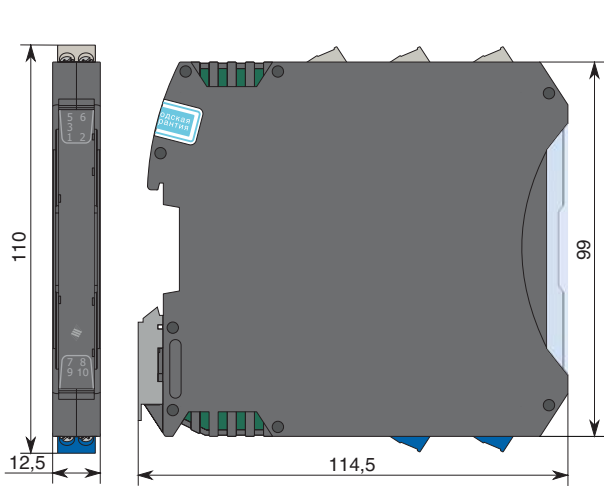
Габаритные размеры барьера в корпусе шириной 12,5 мм с разъемами с винтовыми клемниками
